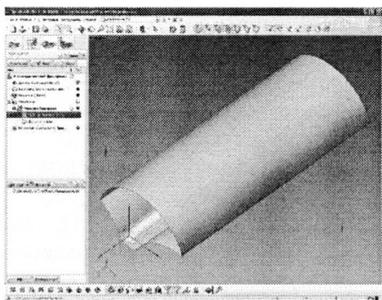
Задання оброблюваної поверхні для операції чорнової обробки
